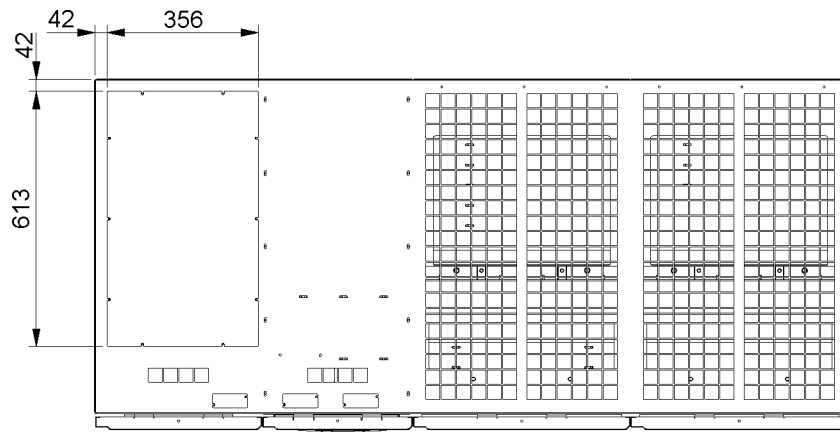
USV-Schrank - Abmessungen (oben)
